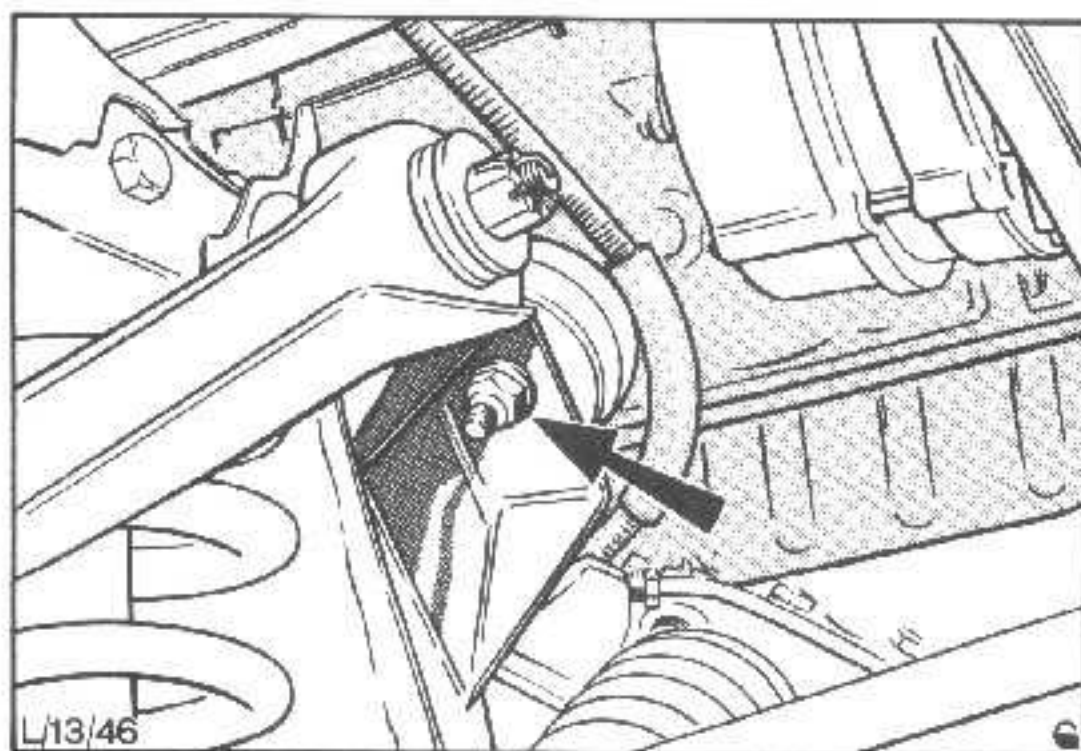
Befestigungsmutter der Motoraufhängung (Rechtslenker gezeigt)
